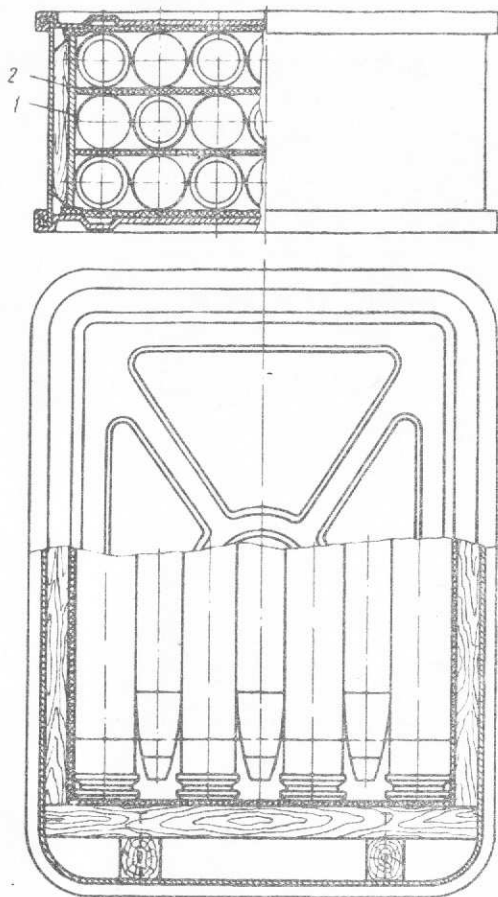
Укупорка патронов в сварно-закатную коробку:
